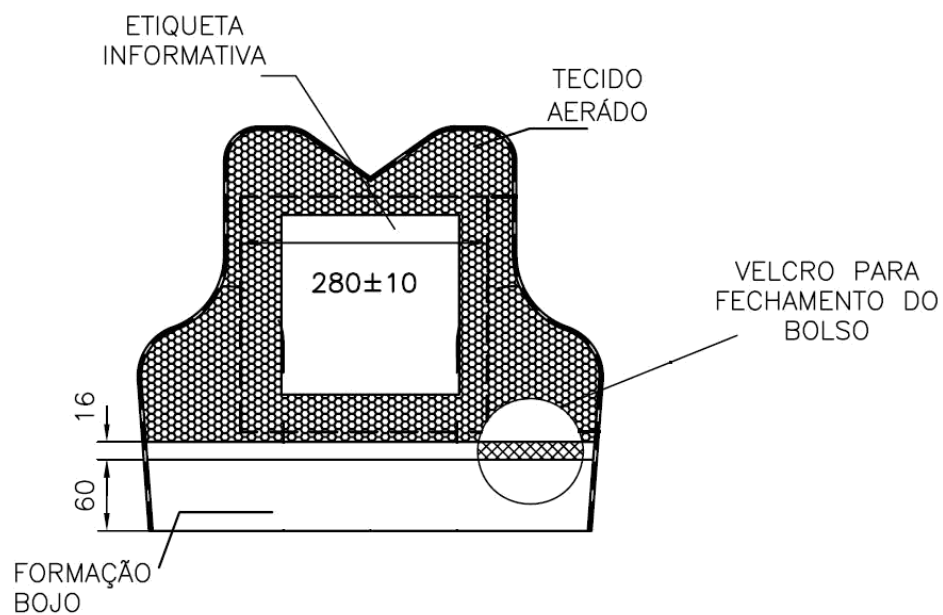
CAPA FRONTAL, FACE INTERNA
